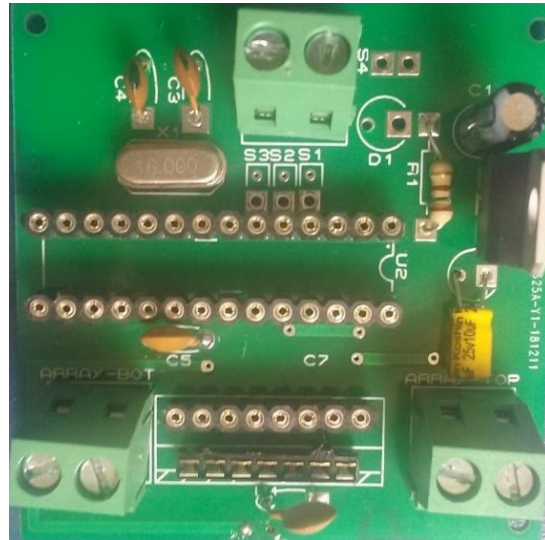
Placa de circuito impresso fabricada na JLCPCB (China), com alguns componentes montados.
